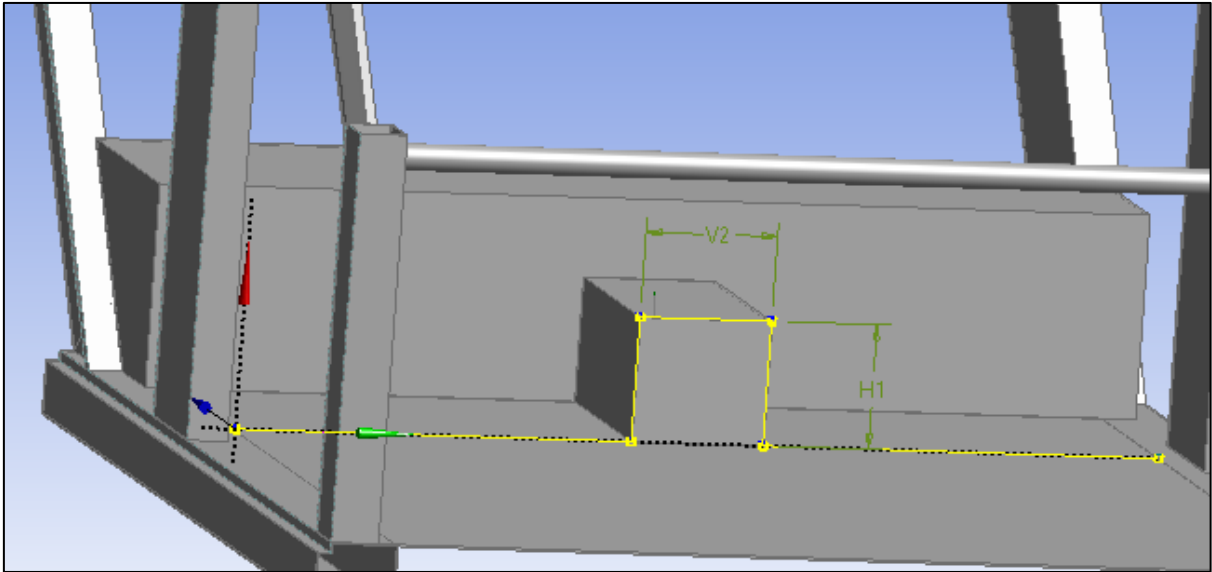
Parâmetros da viga do teto próxima a Coluna “B”
